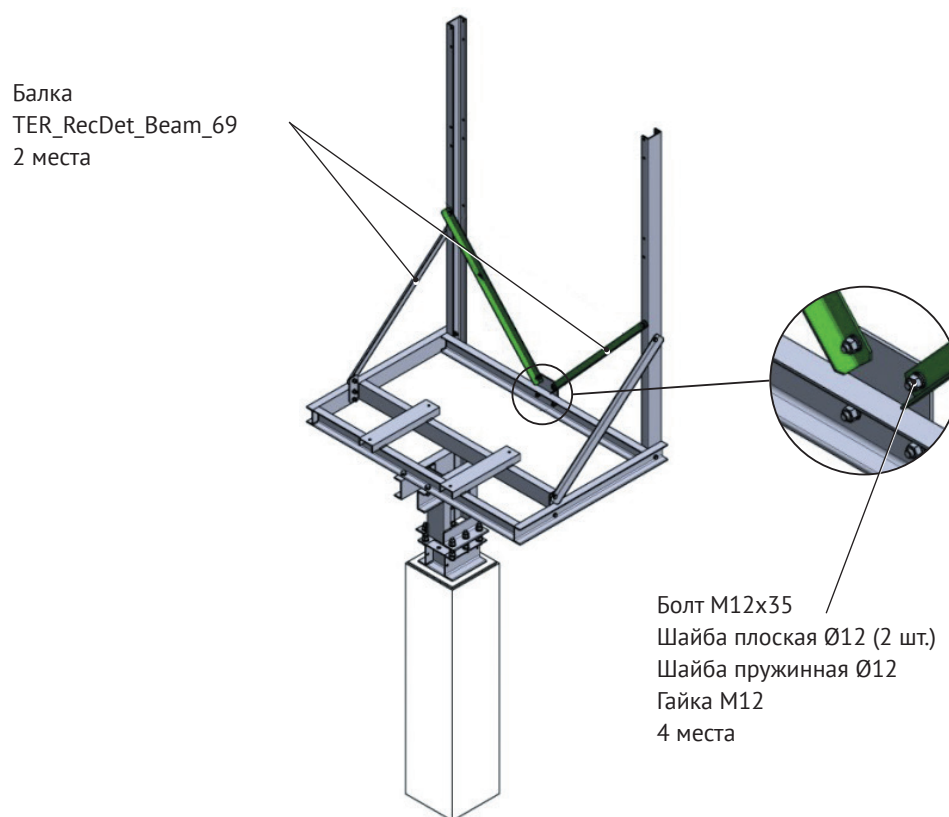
Крепление балок поперечных к стойкам предохранителей
